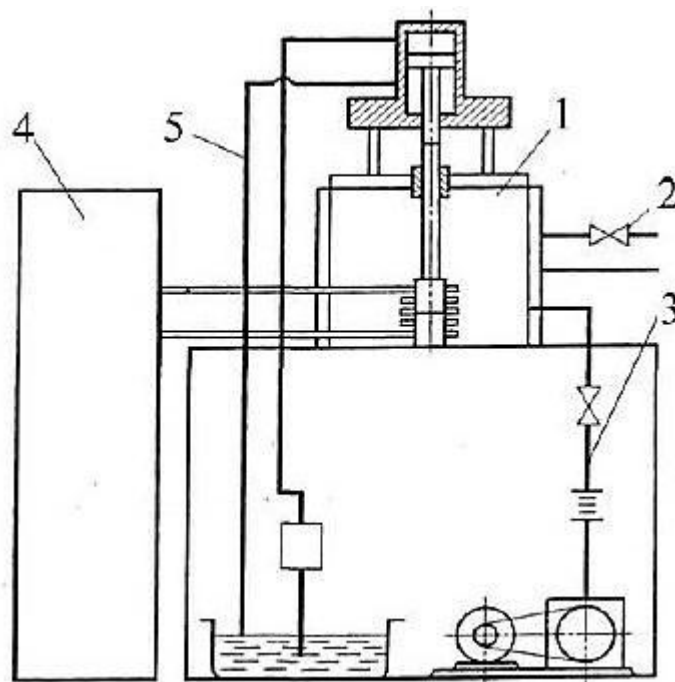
Принципиальная схема установки для диффузионной сварки
